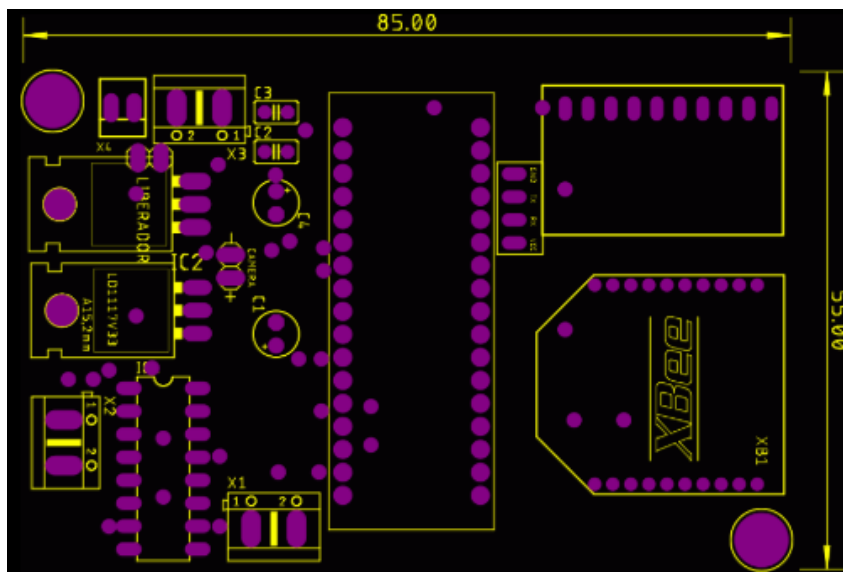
Placa con los componentes que integran el PCB en el software Eagle-Autodesk.
